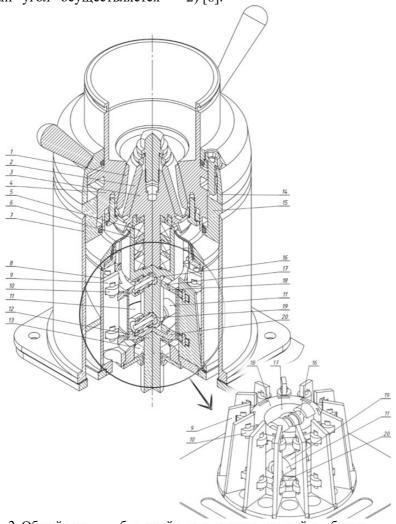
Общий вид разработанной конструкции конусной дробилки
